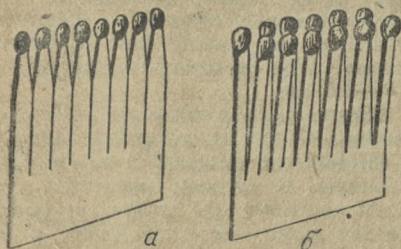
Виды пластинок: а) пластинка с высеченными зубьями; б) пластинка с разведёнными соломками
